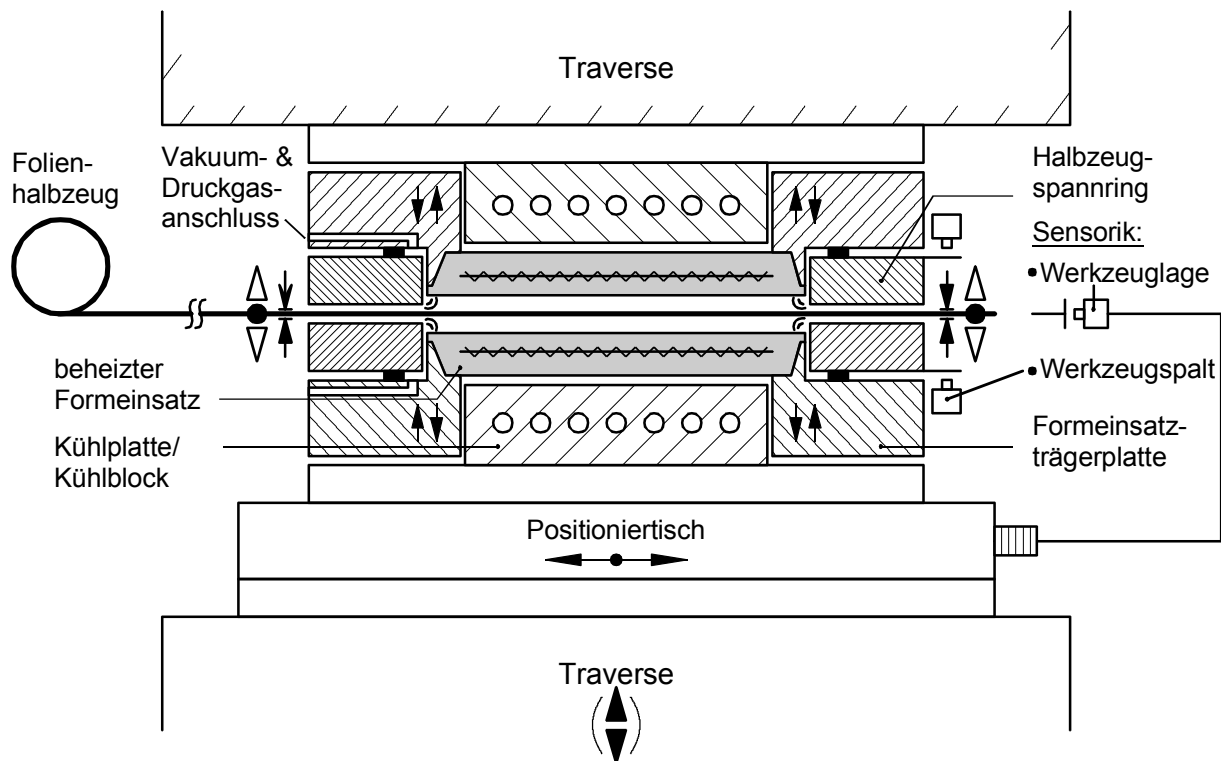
Werkzeugkonzept für das beidseitige Heißprägen
